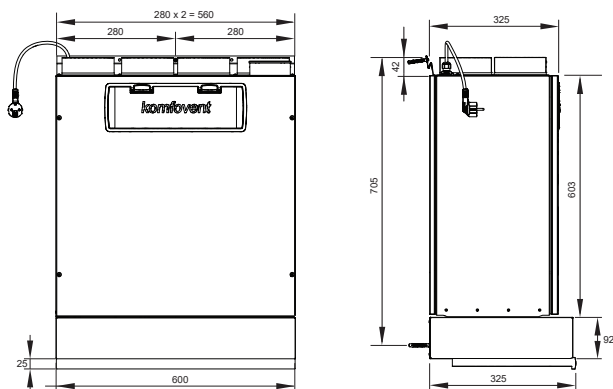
Maße mit der KH 394-12-Dunstabzugshaube
